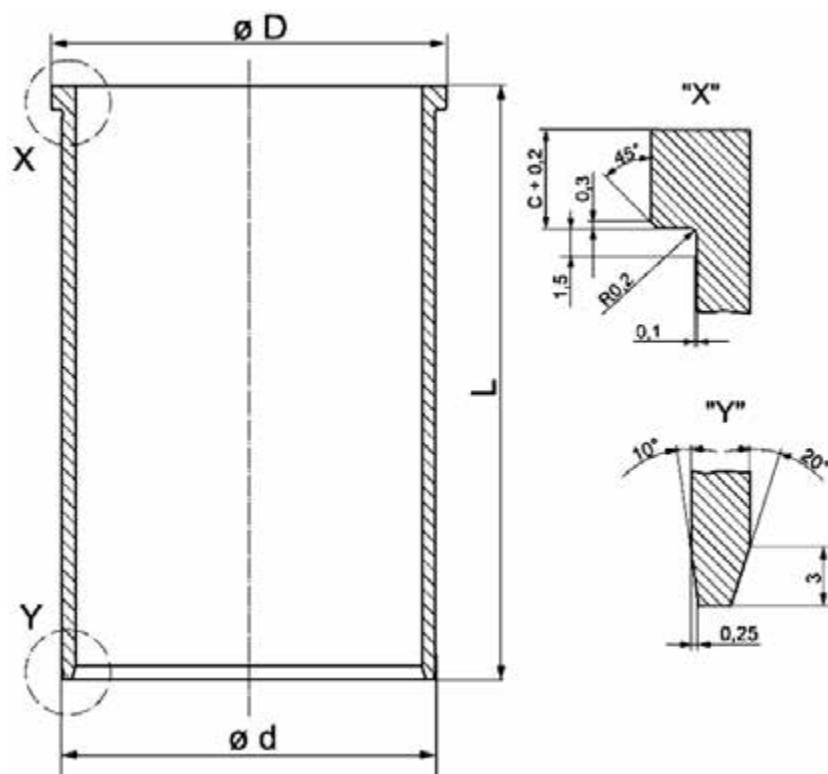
ro-46: Основные размеры, которые следует выдержать при изготовлении чугунной гильзы под запрессовку в блок; источник: MSI
